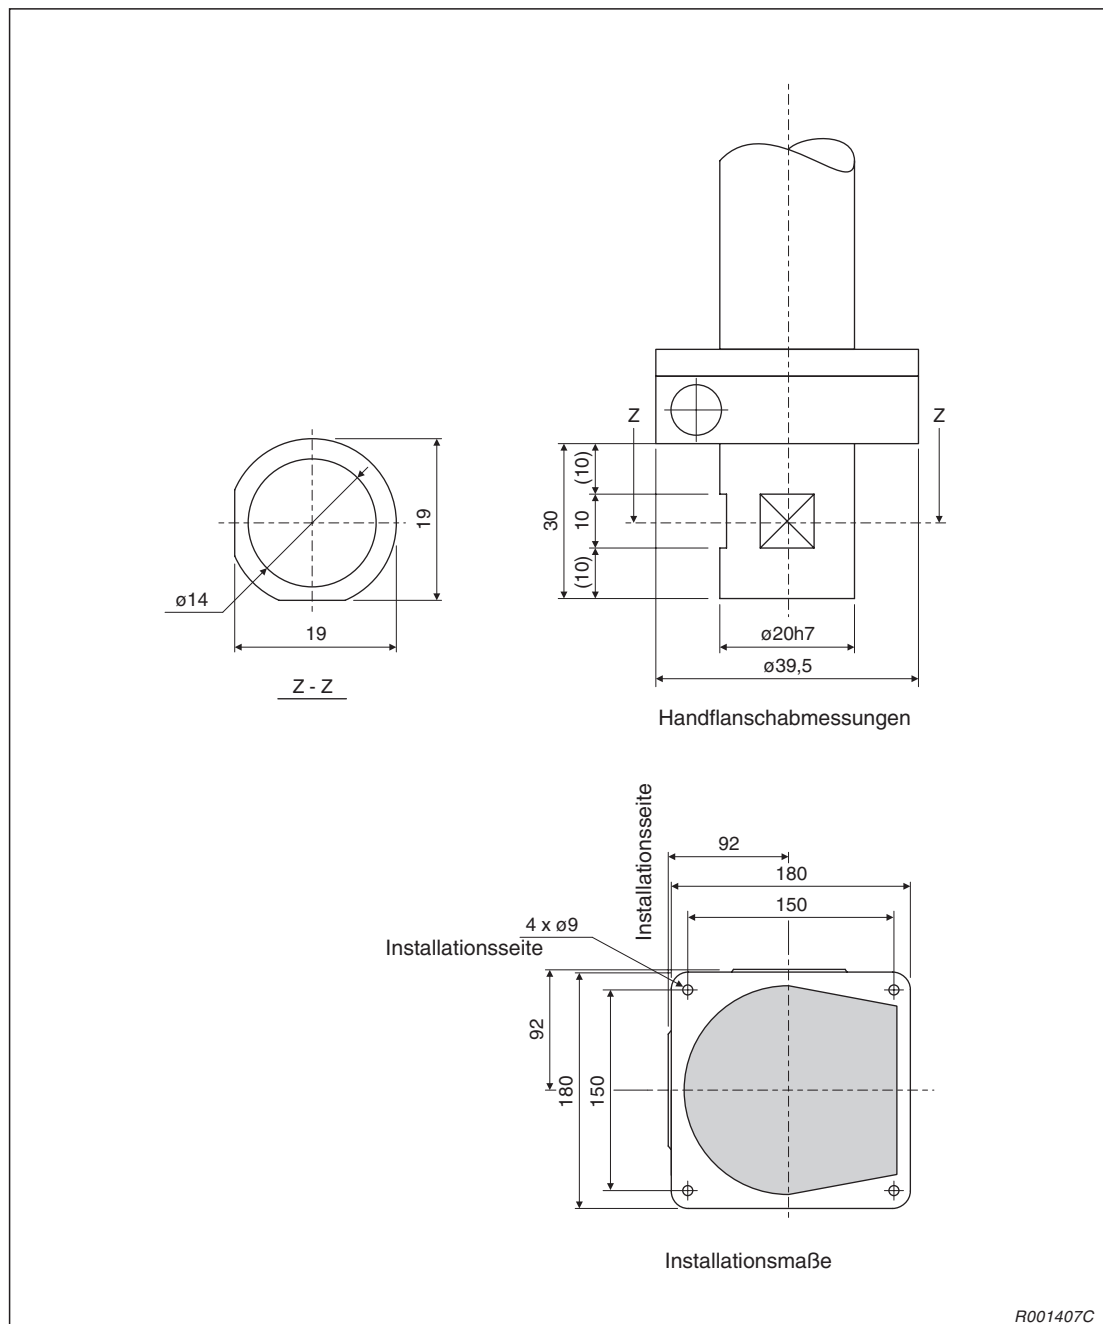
Handflanschabmessungen und Installationsmaße des Roboters RH-6SH
